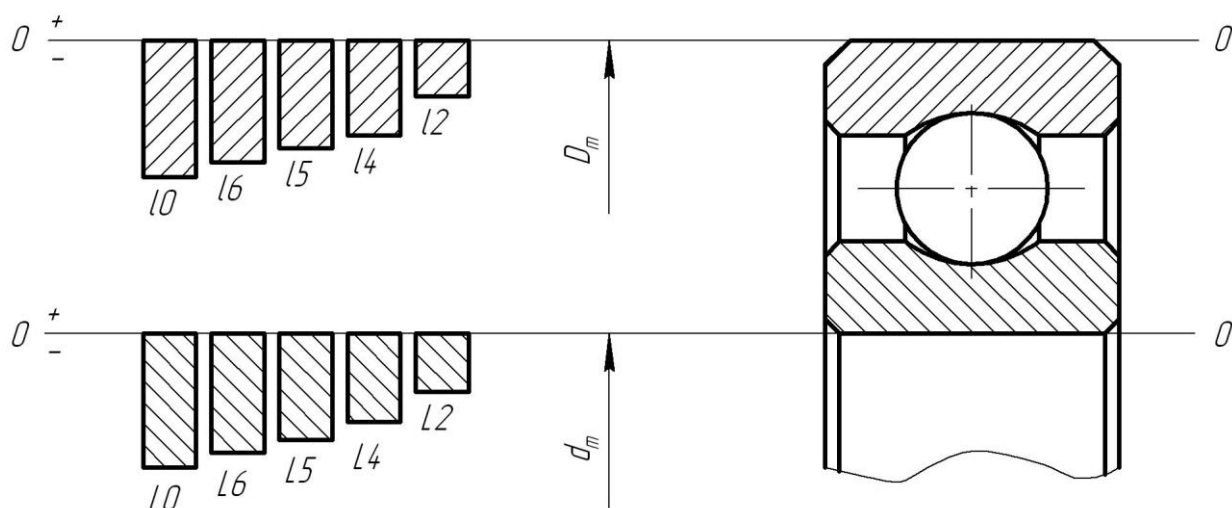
Схема расположения полей допусков на наружный диаметр и диаметр отверстия подшипника
